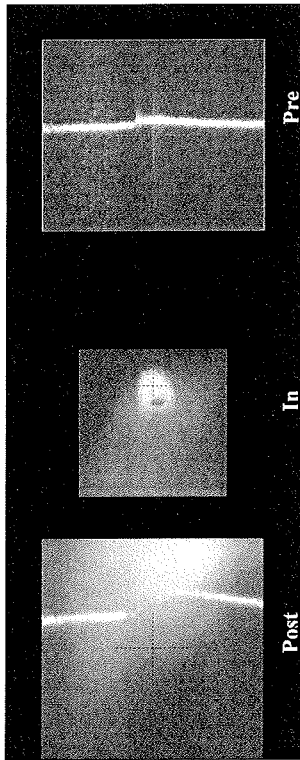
Schweißen eines Realbauteils (Messung S104, Bild-Nr. 129).
